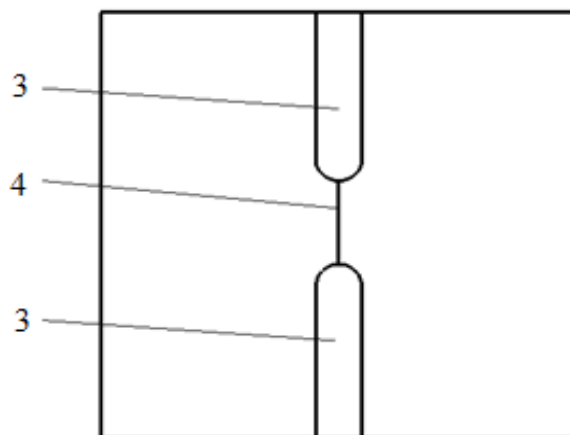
Вид А контрольного образца [44]: 3 – обратный валик шва; 4 – канавка, имитирующая дефект
